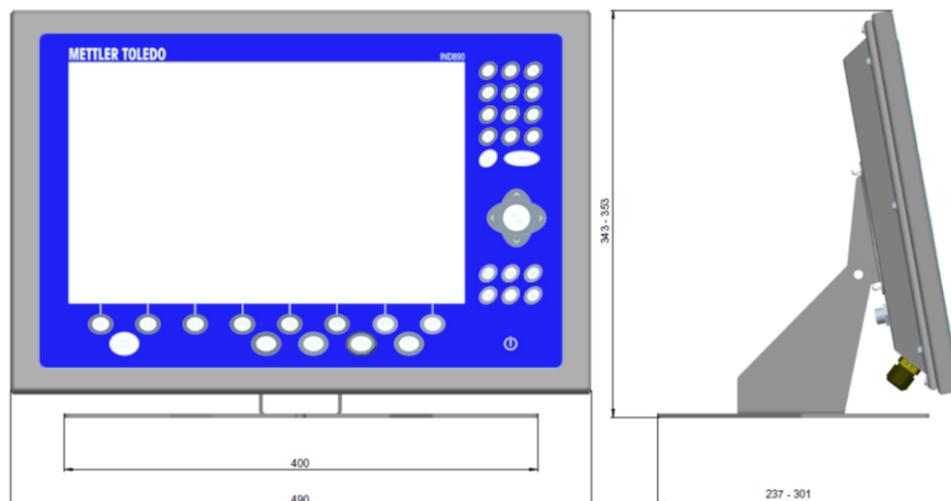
Dimensions IND970-15. Bureau/Mur
